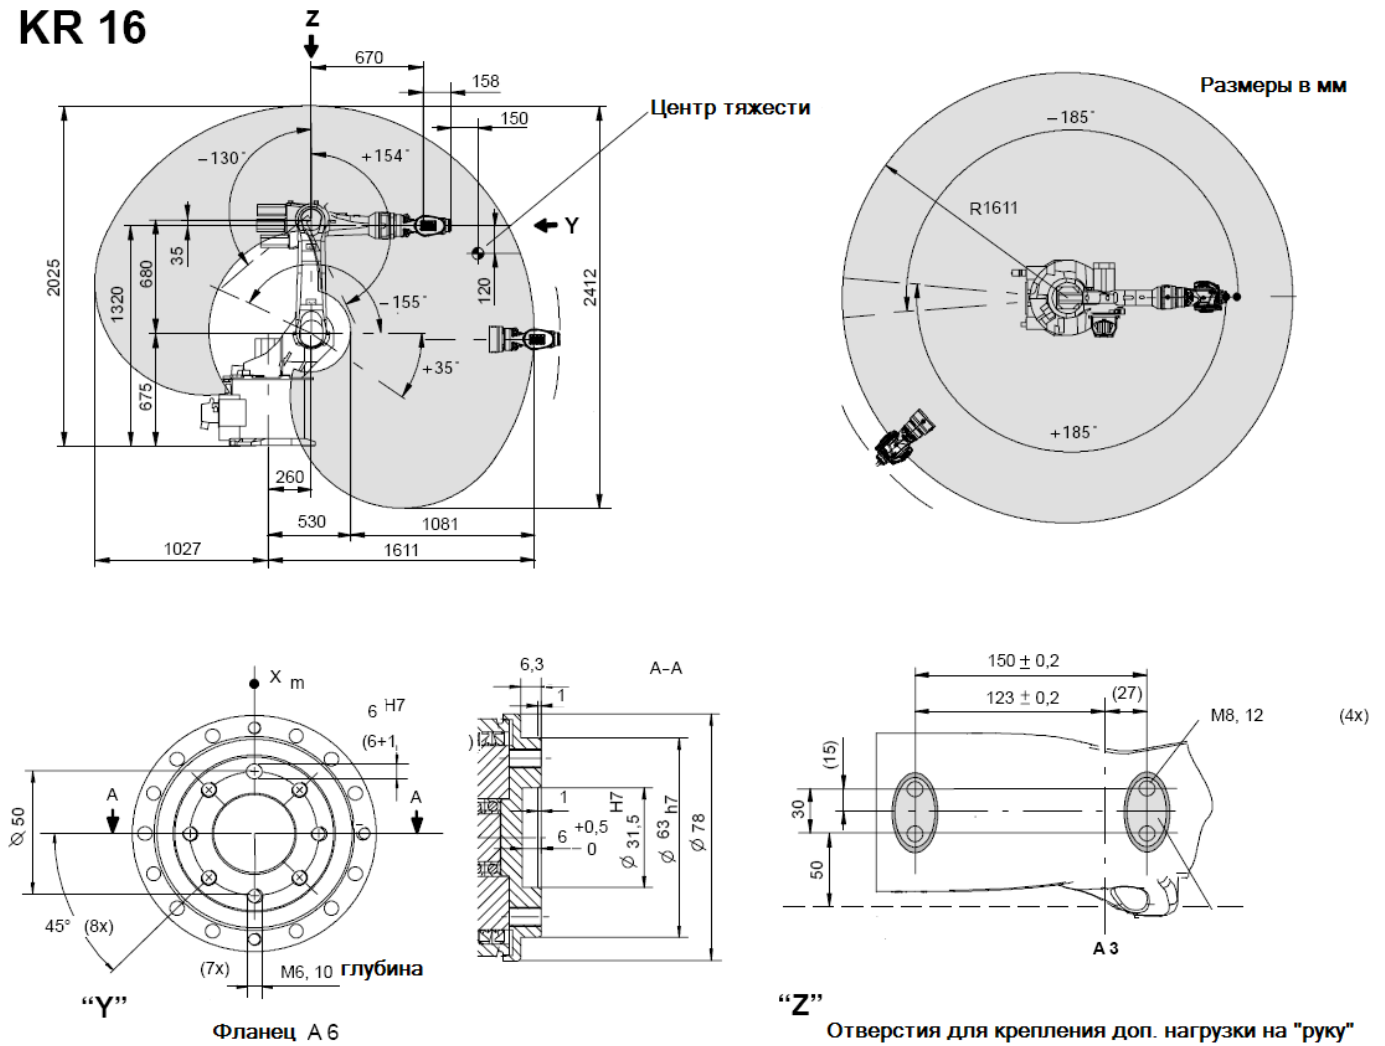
Геометрия рабочей зоны и монтажные размеры ПР КУКА KR16
